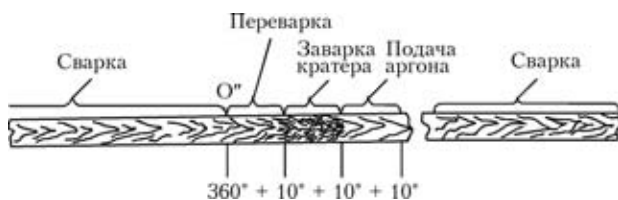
Развернутая схема сварки колпака с патроном (длина сварного шва $L_{ш} = 298,5$ мм)
